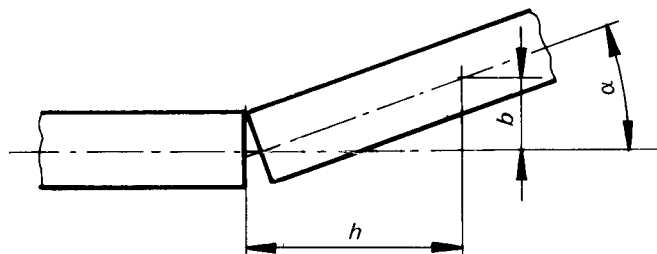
Défaut de contact dû à la déformation d'une machine à souder en bout
